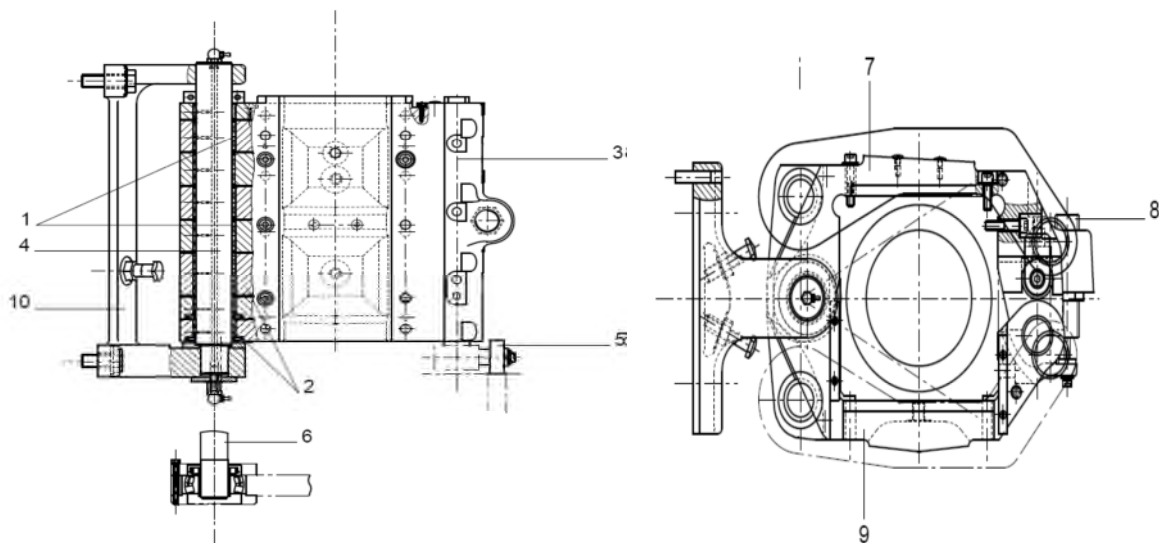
Unité porte moule de la souffleuse SBO4 [2]
